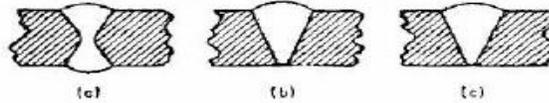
Tipos de Soldadura de Aceros Comunes
